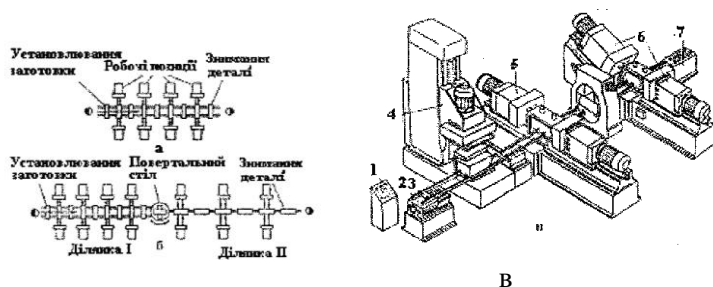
Схеми автоматичних синхронних ліній для обробки корпусних деталей
